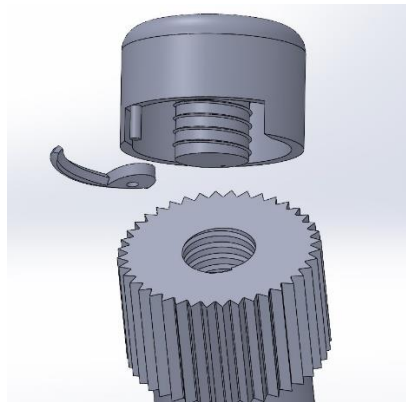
Imagen descriptiva del montaje de la parte superior del producto. Fuente: elaboración propia.
